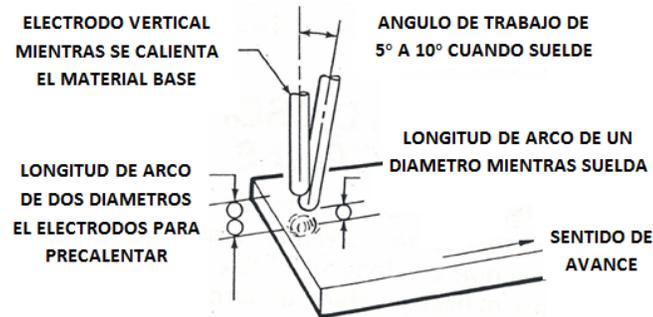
CORDON DE SOLDADURA
